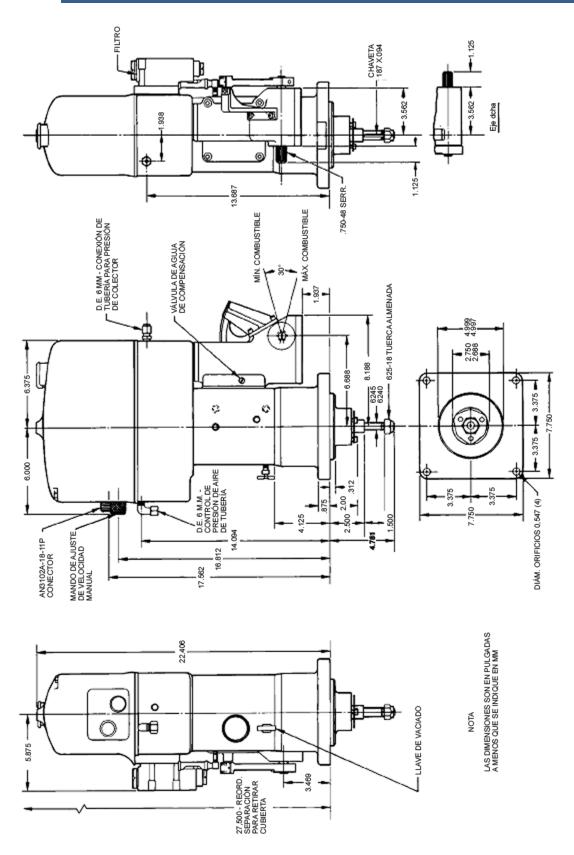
Plano esquemático de PGA con servo rotatorio de 12 pies-libra y base UG-40 (No usar para construcción).
